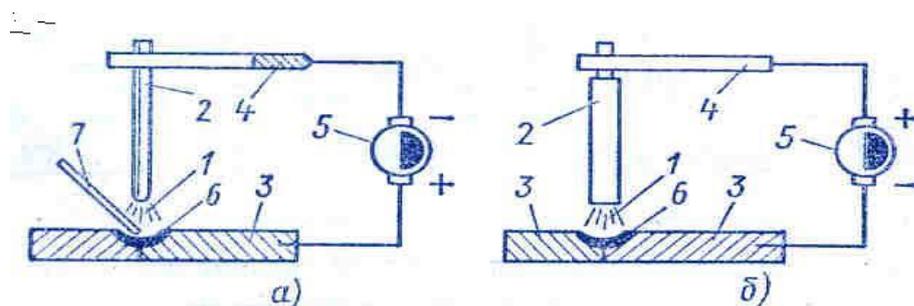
Схема ручного процесса дуговой сварки
